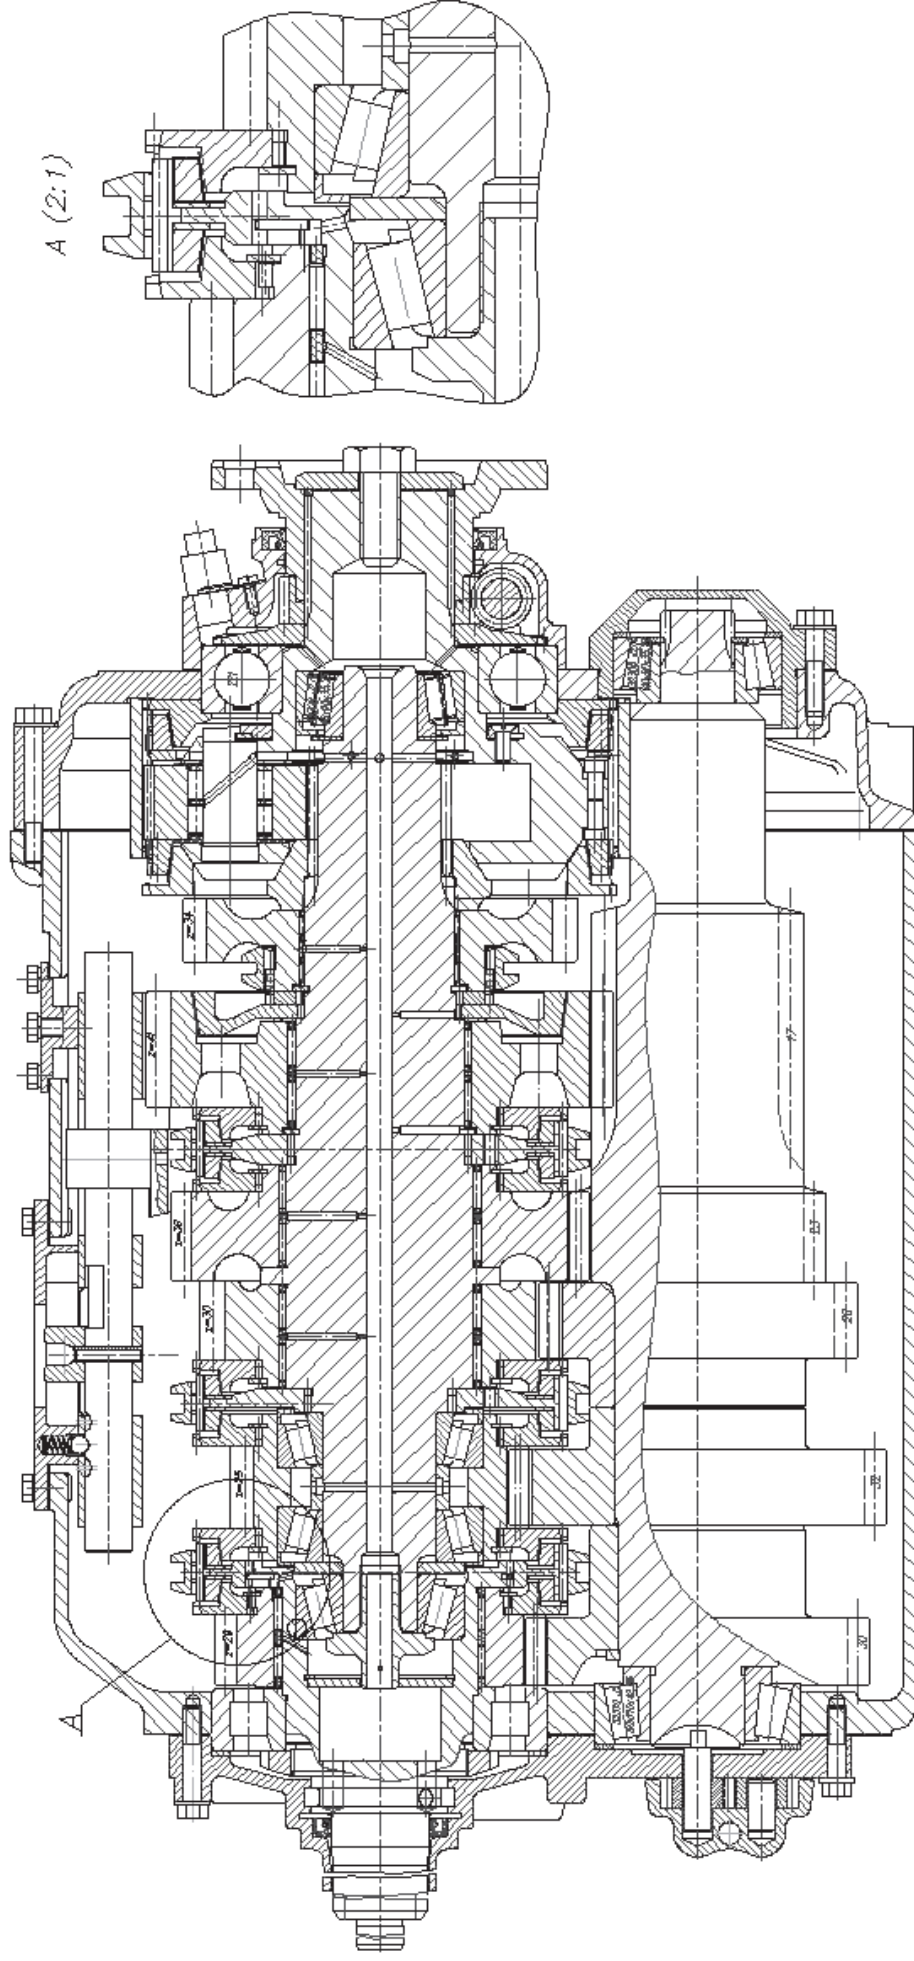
Коробка передач ТМ16-2000 (продольный разрез)
